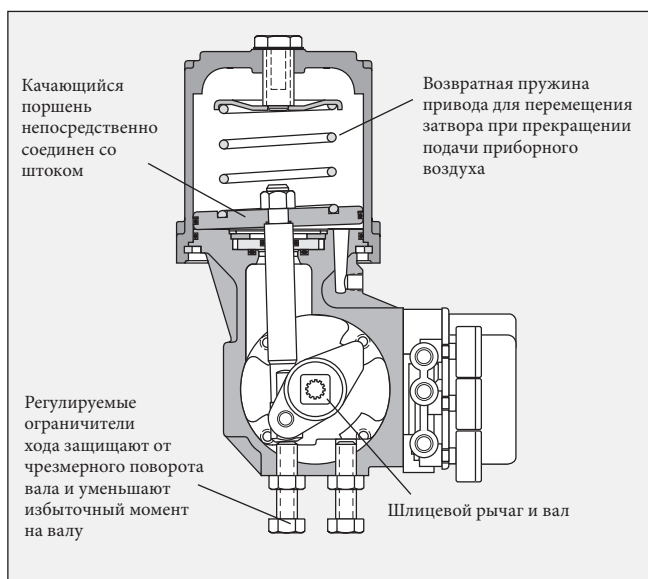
Поворотный поршневой привод с возвратной пружиной
